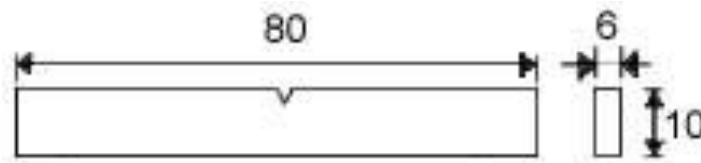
Dimensões, em mm, do corpo de prova de impacto
